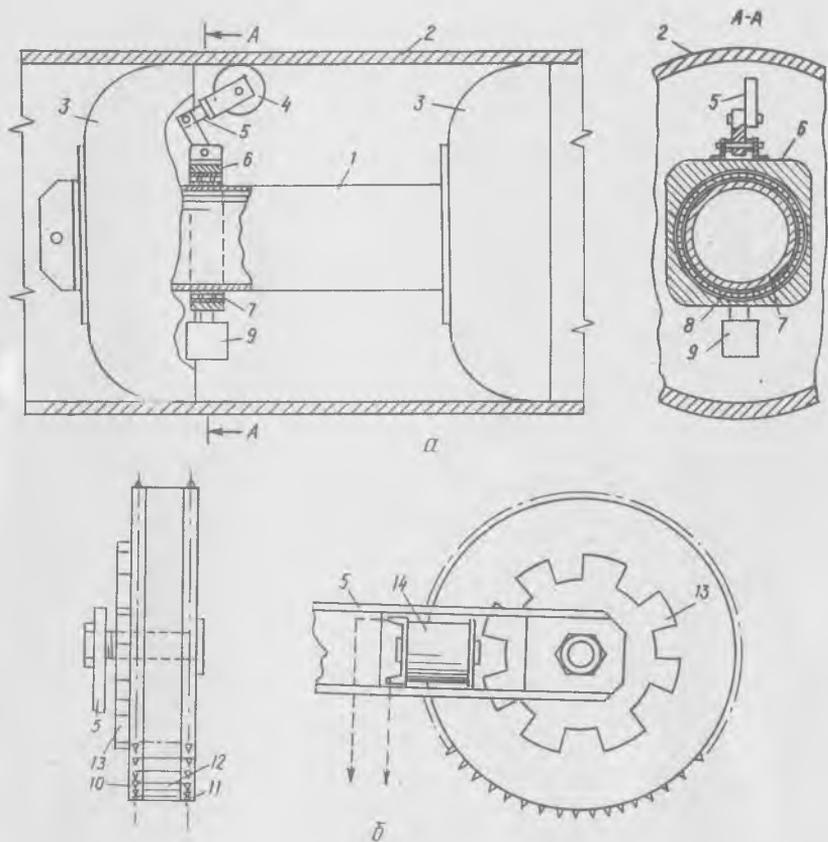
Общий вид скребка (а) и конструкция магнитного колеса (б)
